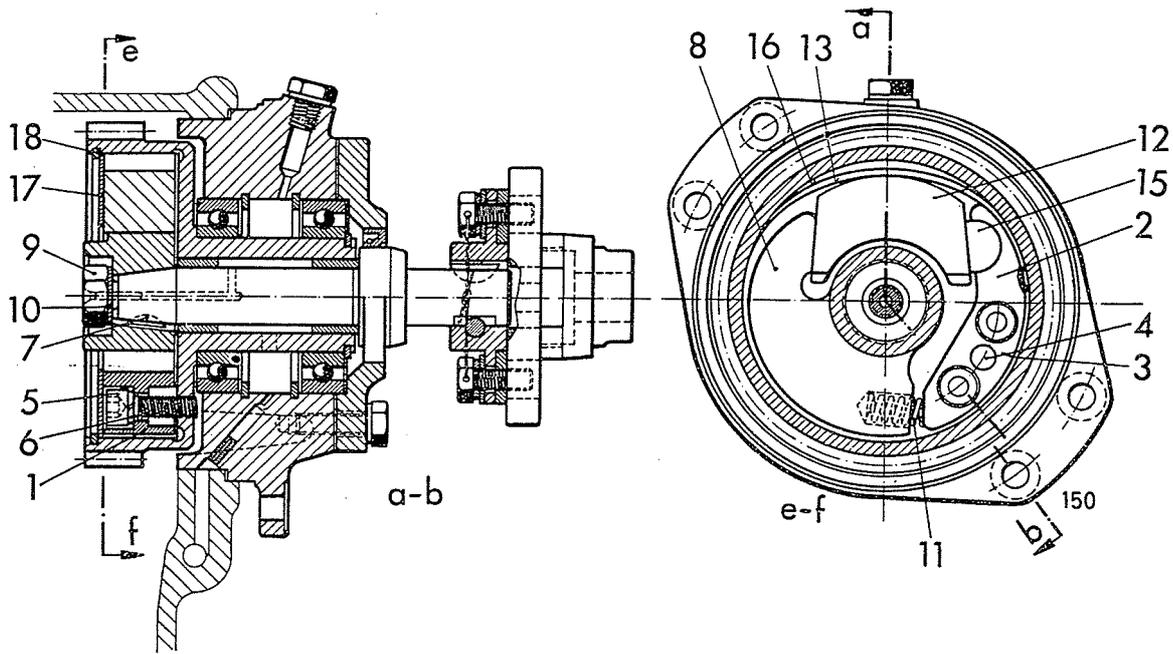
Spritzversteller F 4-6L 514 mit einem Fliehkraftgewicht und zwei Kugellagern
